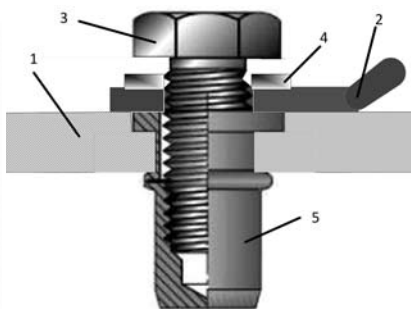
Болтовое соединение кабельного наконечника с шиной с помощью гайки-заклепки. 1 - медная шина; 2 - кабельный наконечник; 3 - болт; 4 - корончатая шайба; 5 - гайка-заклепка
